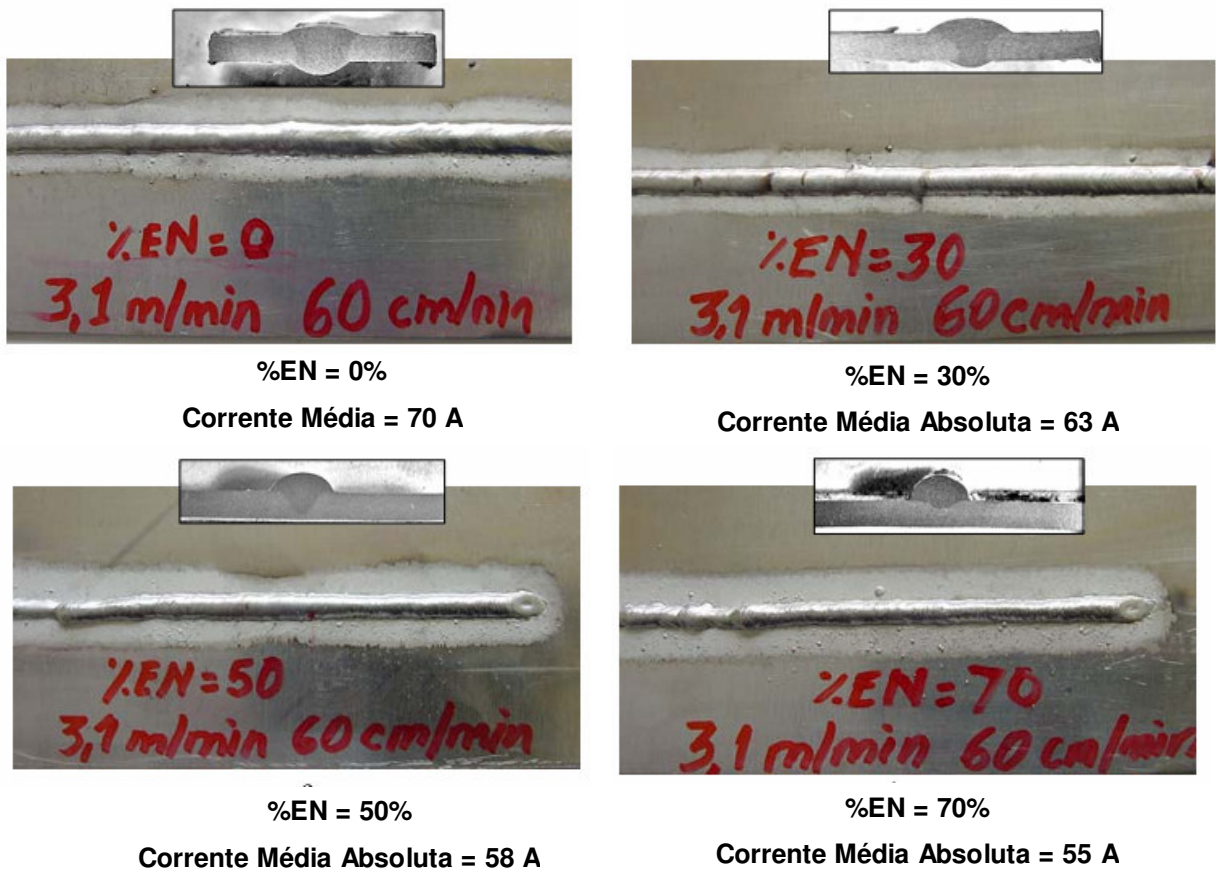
Cordões de solda sobre chapas de alumínio 1200, utilizando processo MIG Pulsado CA [36].
